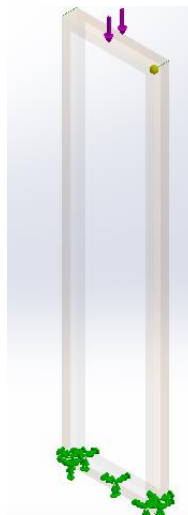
Cordones de soldadura críticos en la parte fija.
